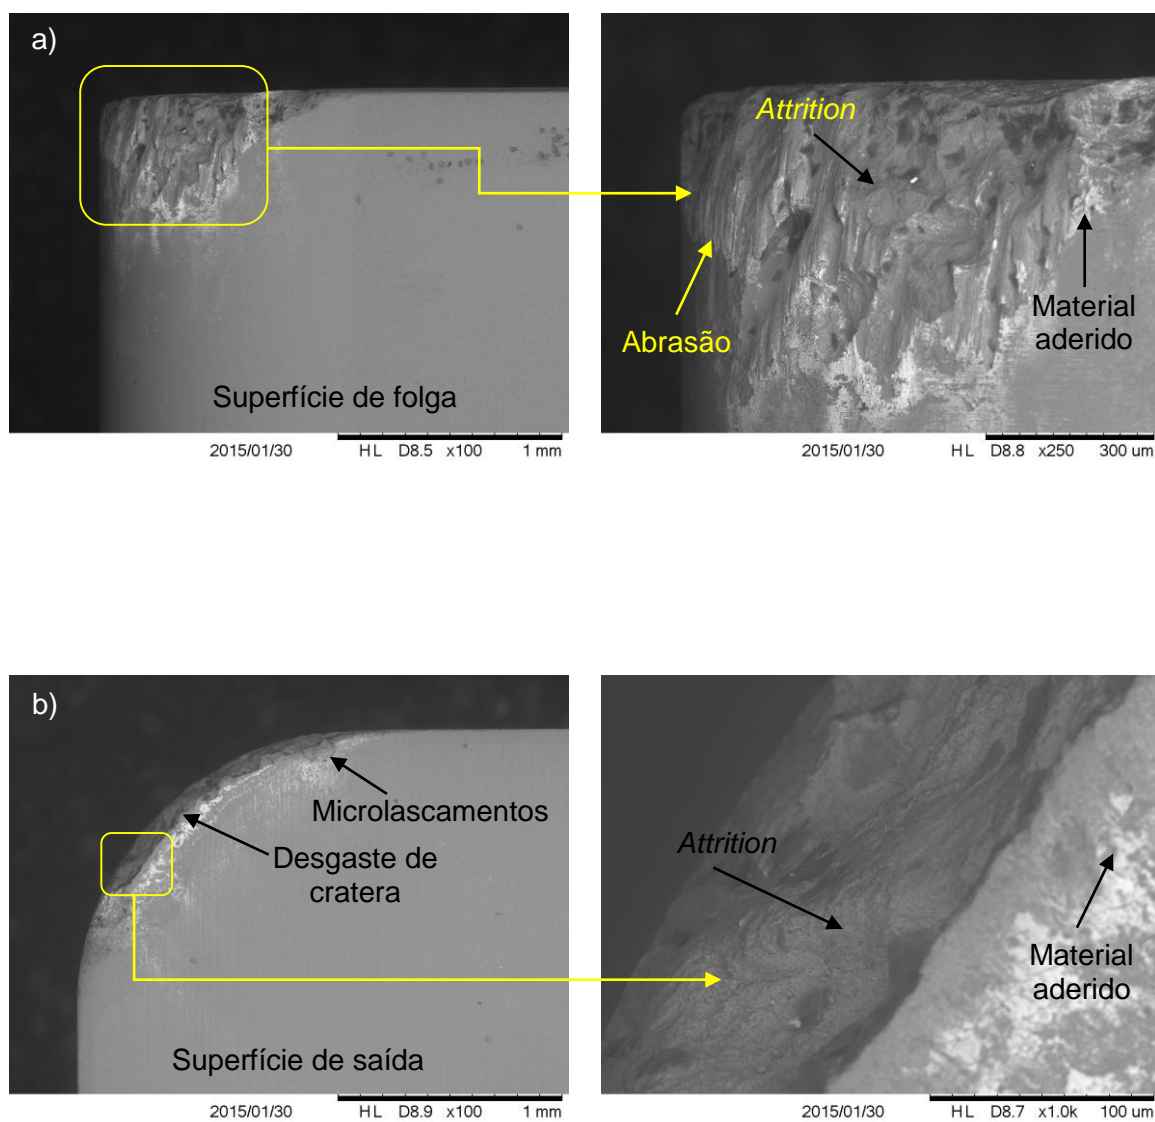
Fotografias obtidas através do MEV das ferramentas SiAlON após a usinagem do Inconel 718 com aplicação de fluido de corte LB 2000 + 20% grafite por MQF. (a) superfície de folga e (b) superfície de saída
